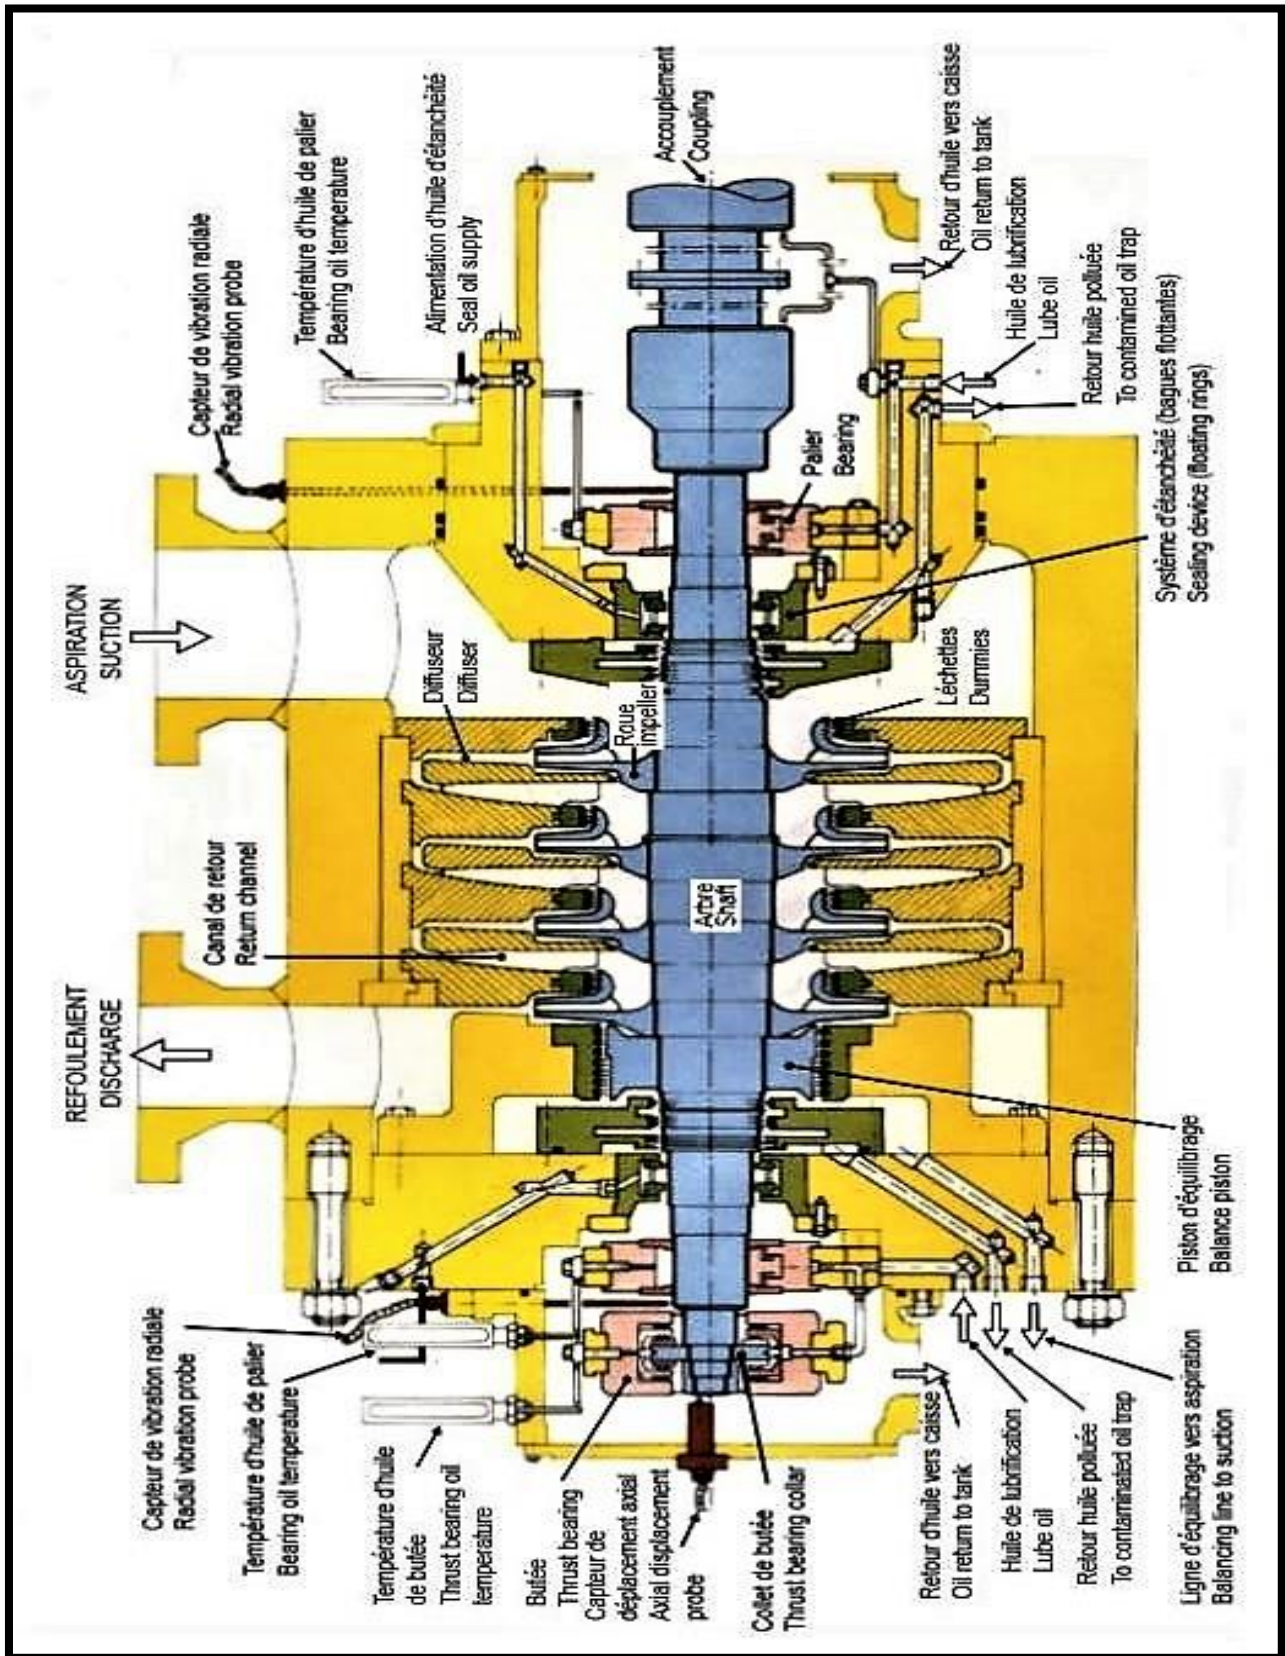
coupe longitudinale d'un compresseur centrifuge [13]
